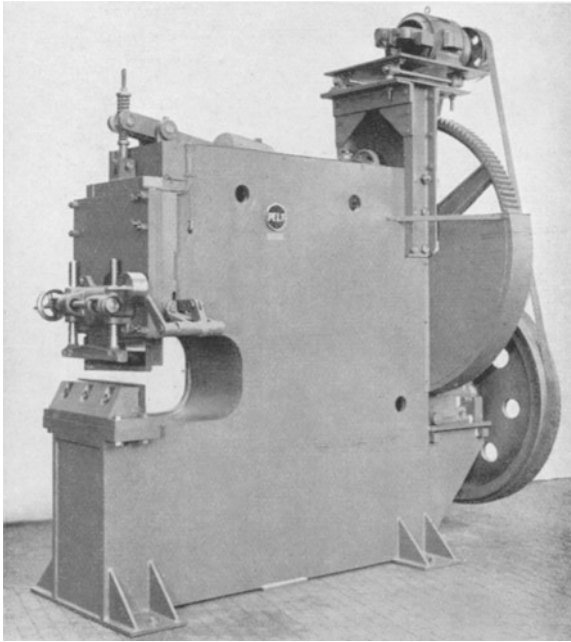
Geschweißte Stahlkonstruktion einer Blechscherer.
